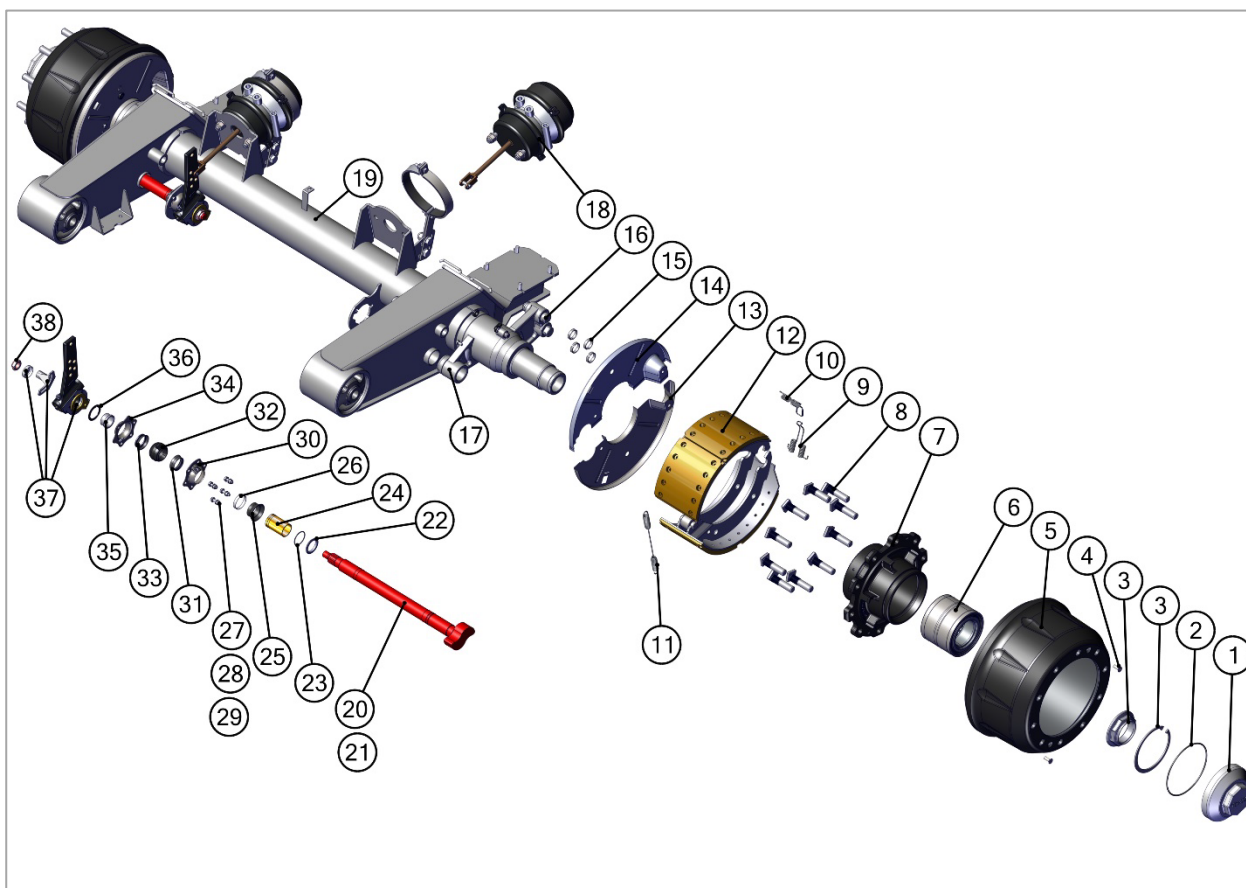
Взрыв-схема оси полуприцепа с барабанными тормозами.
